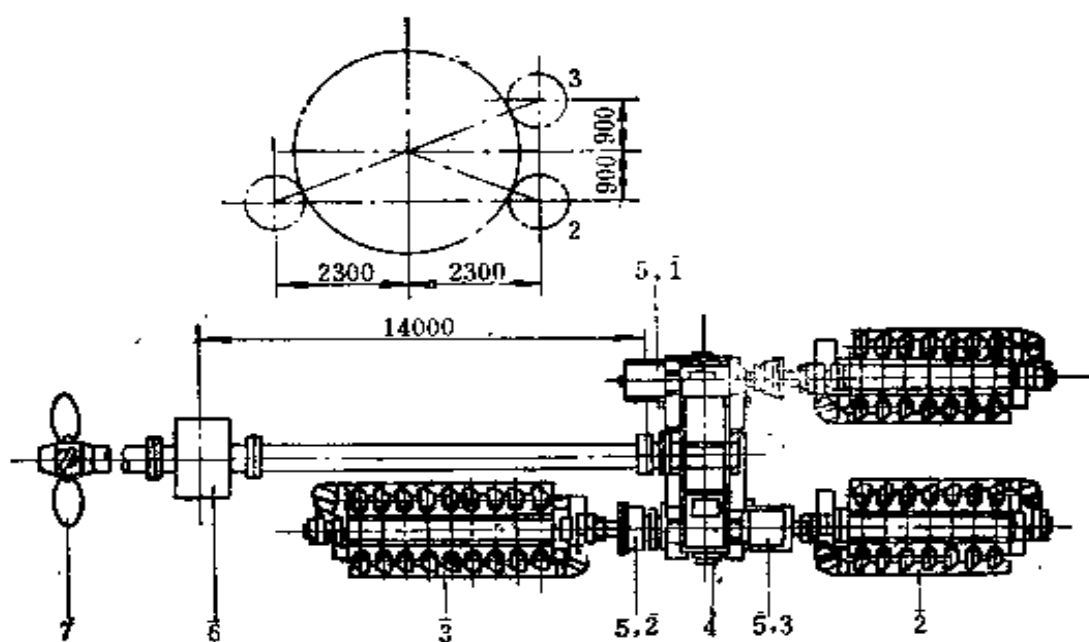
采用三台柴油机 46000PS 的三机并车齿轮减速装置
